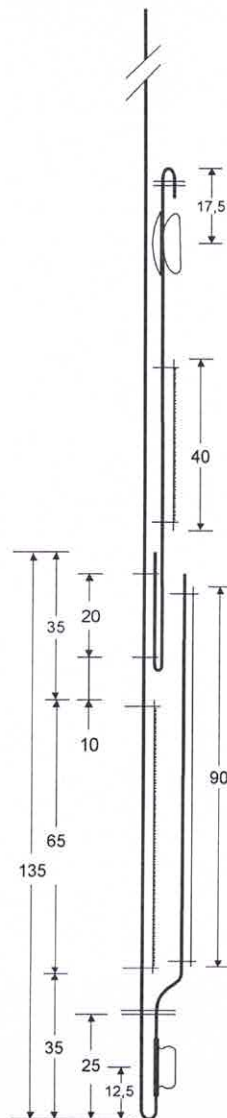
MONTAGEM DO TIRANTE (MEDIDAS EM MM)
